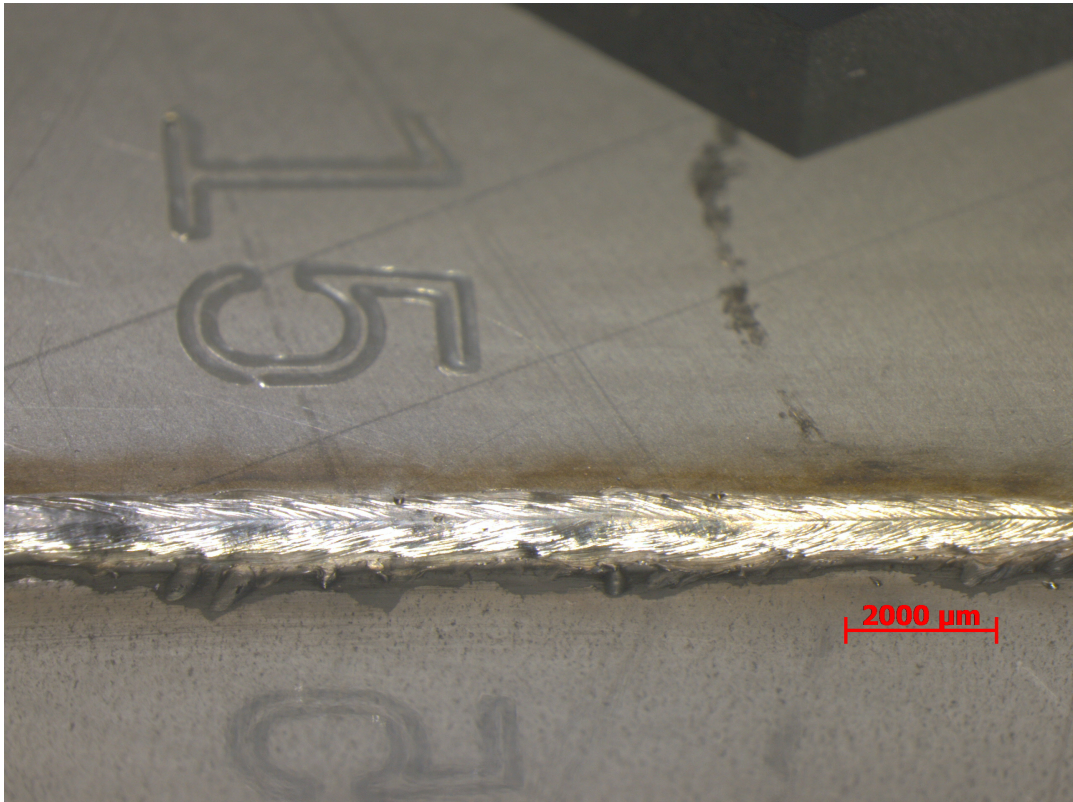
Vue macroscopique de l'endroit du cordon de soudure débouchant.
